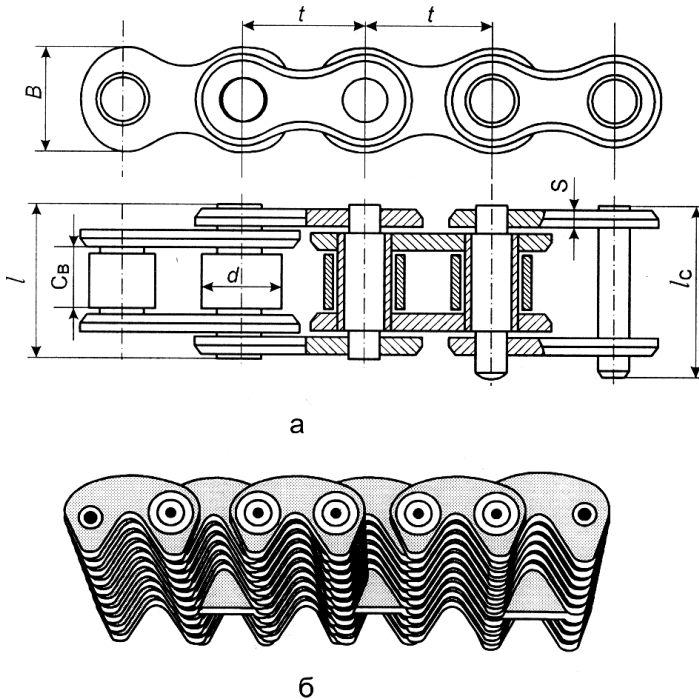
Приводные пластинчатые цепи: а — роликowe; б — зубчатые
